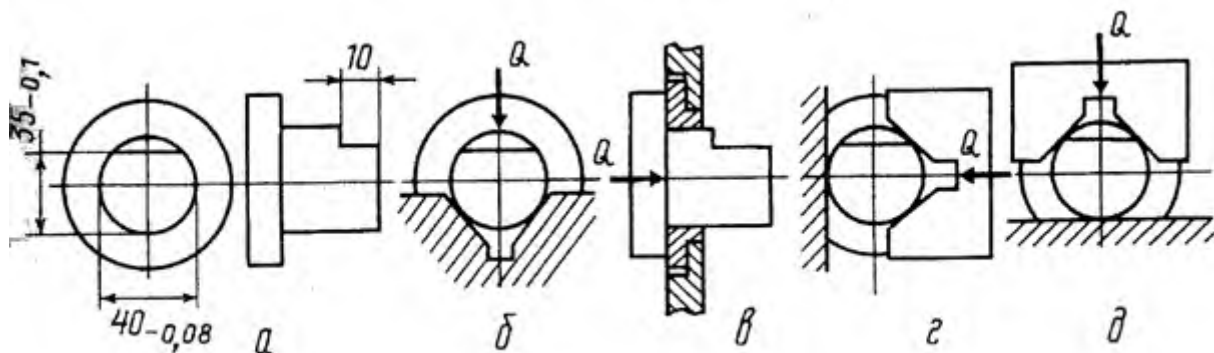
Варианты выбора рациональной схемы базирования и закрепления заготовки [2]
